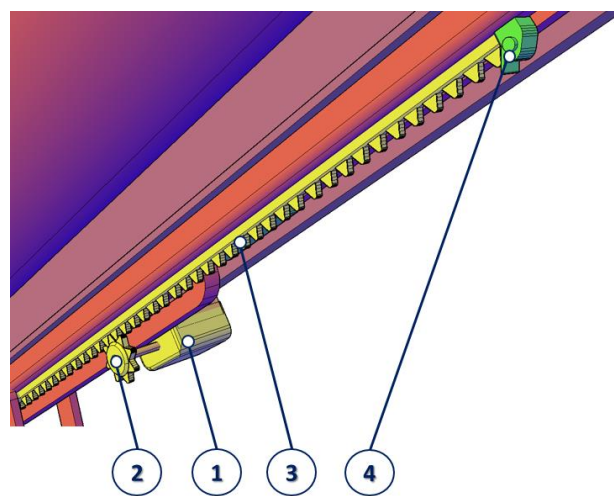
Конструкция привода: 1- мотор-редуктор; 2- зубчатое колесо; 3 – зубчатая рейка; 4- переключатель концевой
